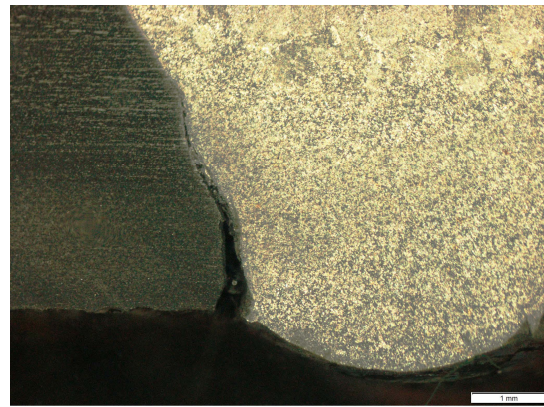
Probe G04-05, Schweißnaht FAT 71, Vergrößerung
